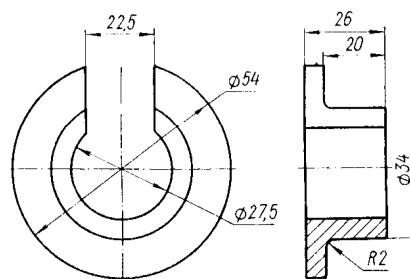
Оправка для спрессовки подшипникового узла с полуоси
